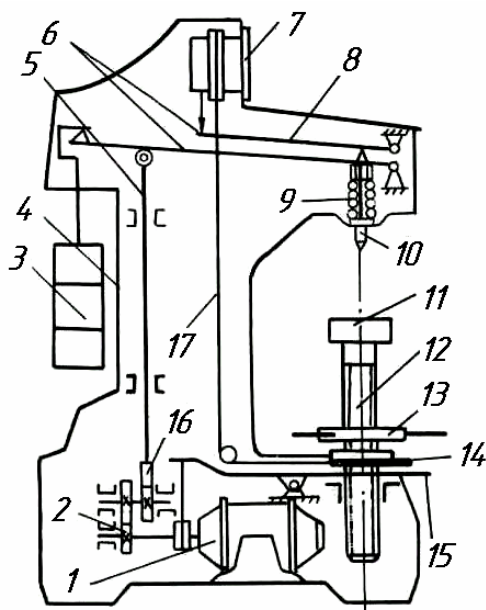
Схема пресса Роквелла: 1 — электродвигатель; 2 — червячный редуктор; 3 — грузы; 4 — корпус; 5 — шток; 6 — грузовой рычаг; 7 — индикатор; 8 — рычаг; 9 — пружина; 10 — индентор; 11 — подъемный столик; 12, 13 — пара винт-маховик; 14 — механизм подъемного столика; 15 — кнопка «Пуск»; 16 — кулачковый блок; 17 — трос управления индикатором
